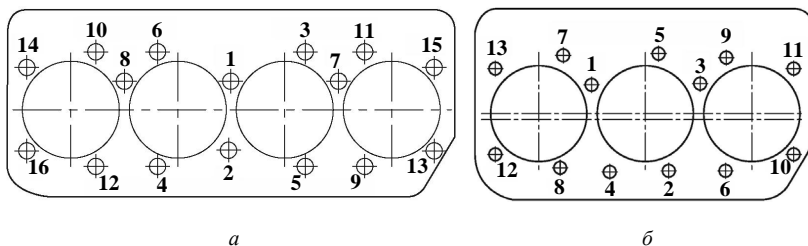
Схема затяжки болтов головки блока цилиндров двигателей Д-243, Д-245 (а) и Д-260 (б)
